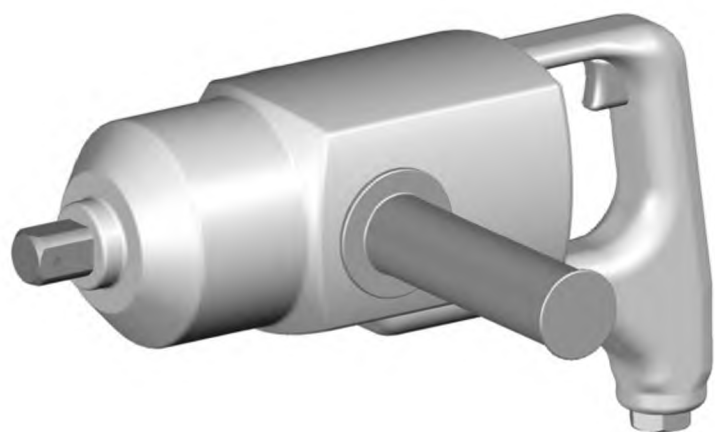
Ударный/импульсный гайковерт с дугообразной основной рукояткой и прямой поддерживающей рукояткой
